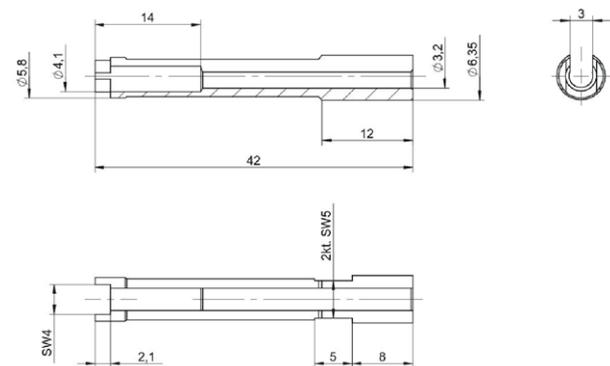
Demontagewerkzeug für Kabel Typ 1300A49
